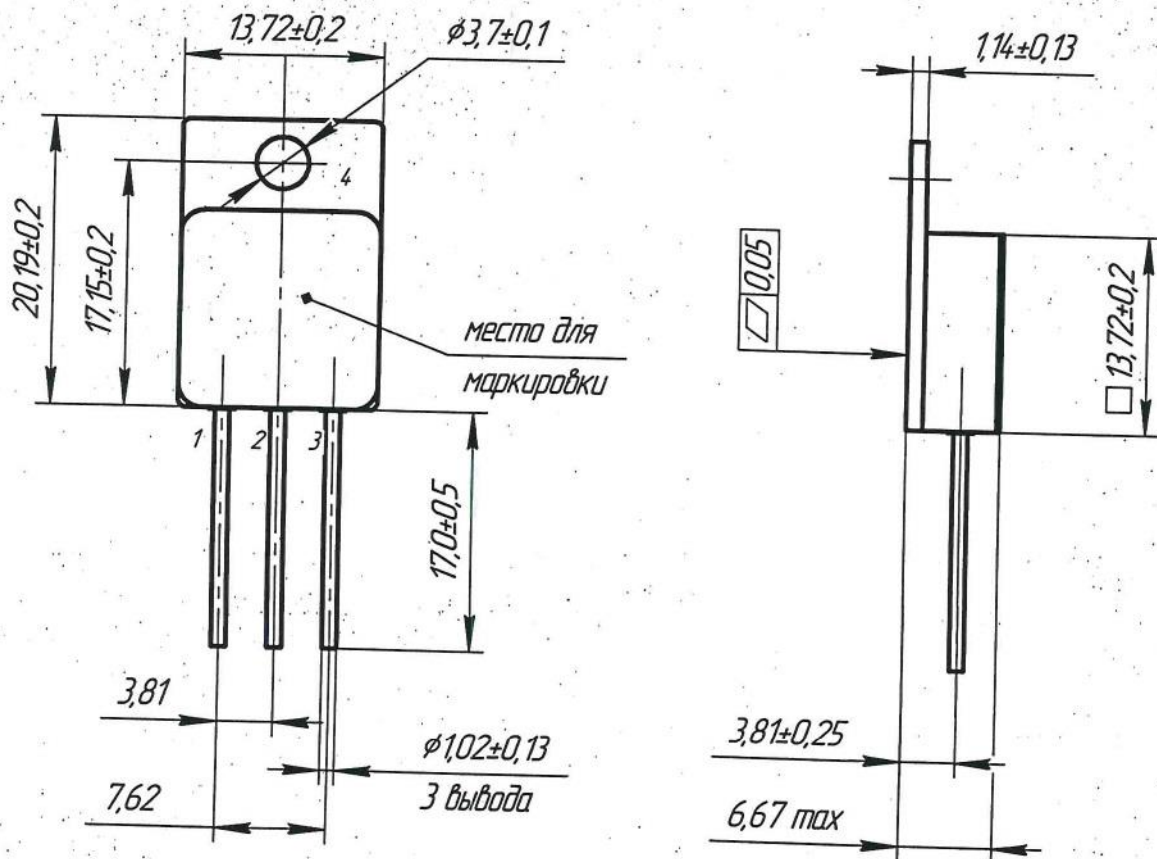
Габаритный чертеж корпуса КТ-97А-5.01
